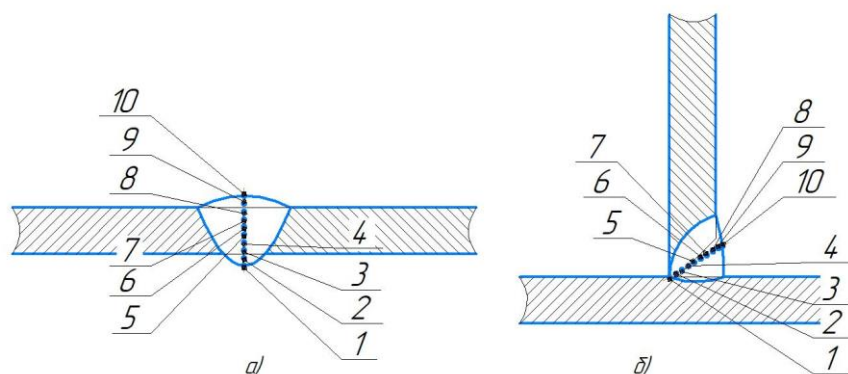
Точки исследований напряжений сварных соединений: а – стыковой шов; б – тавровый шов
